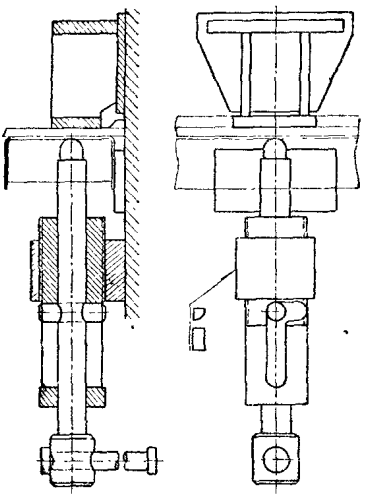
Быстродействующий прижим с поворотным корпусом.
